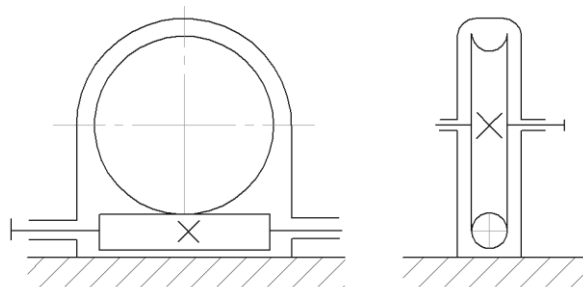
Одноступенчатый горизонтальный червячный редуктор с нижним расположением червяка
